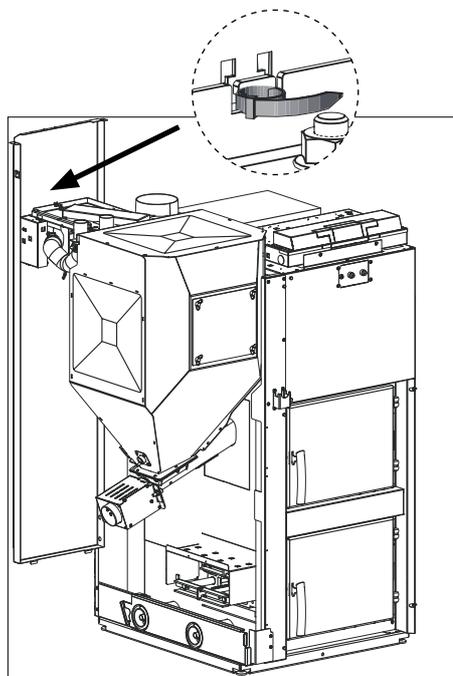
Fissare temporaneamente la parete posteriore con fascette per cavi a circa 25 cm dal pavimento
